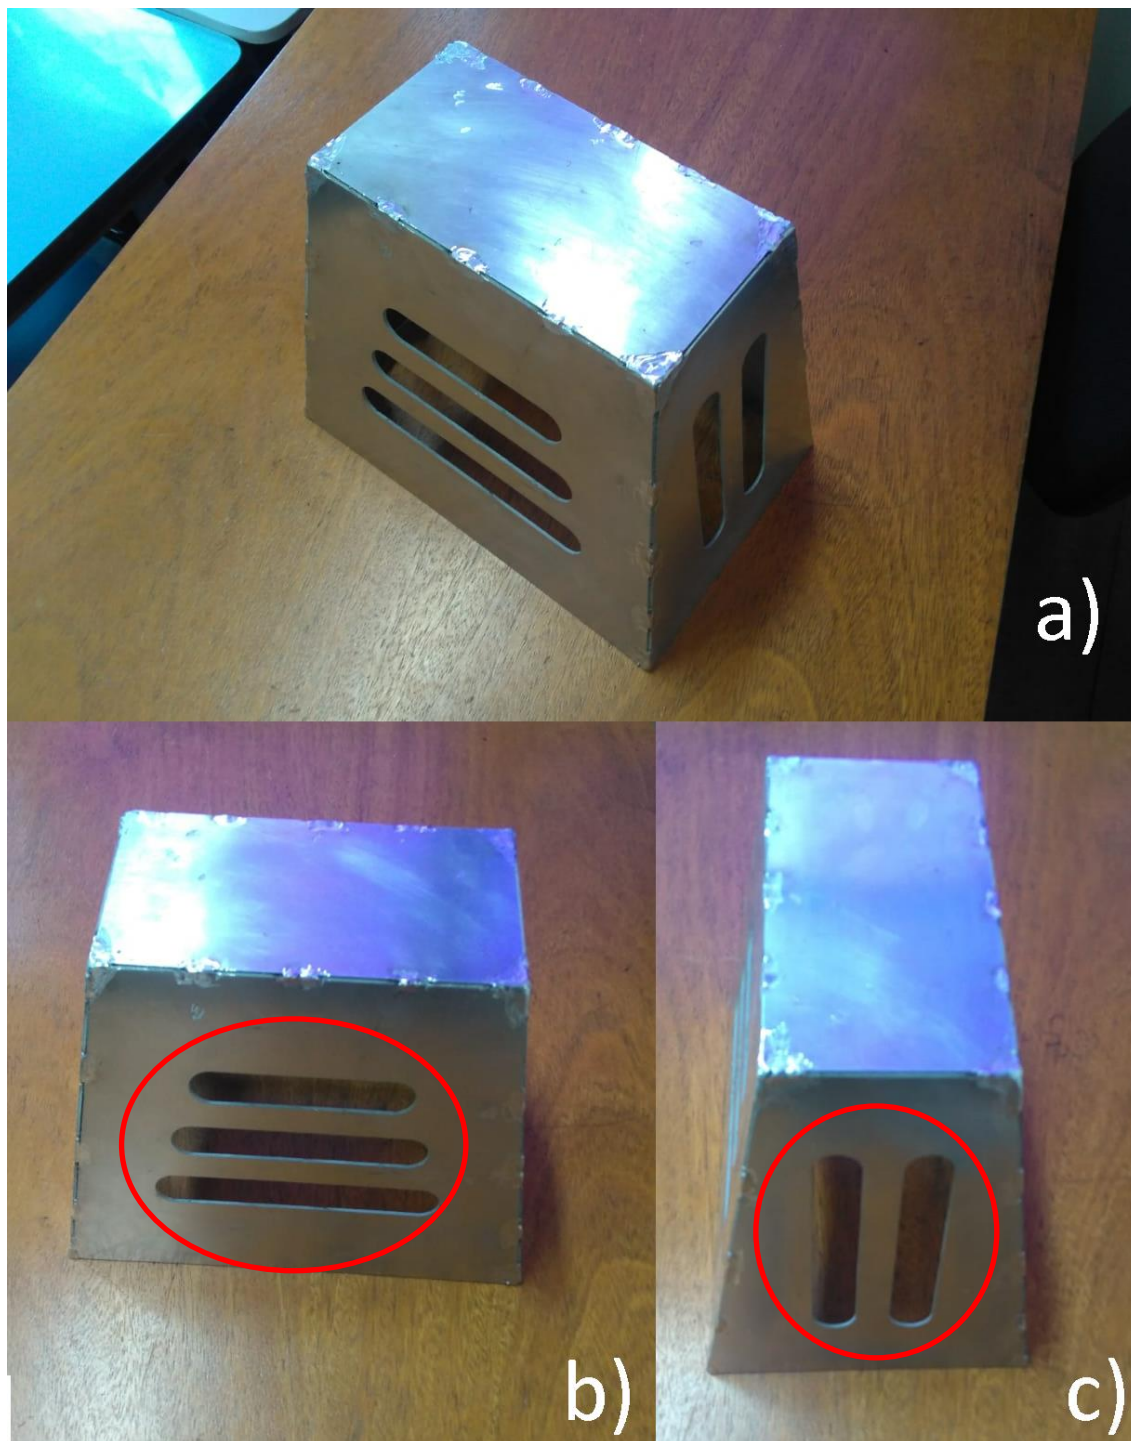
12 Atenuador de impacto após soldagem. a) Vista isométrica, b) vista da parte superior e c) vista lateral.
